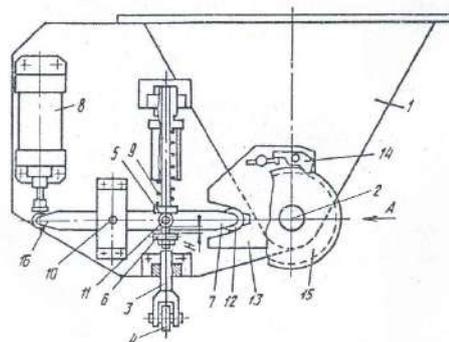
Устройство для подачи порошкообразных материалов в качающийся кристаллизатор [8]: 1- бункер; 2- шнековый питатель; 3- штанга-толкатель; 4- ролик; 5 и 6- упоры; 7- двулучий рычаг; 8- пневмоцилиндр; 9- пружина; 10- ось; 11 и 12- ролики; 13- коромысло; 14- собачка; 15- храповое колесо; 16- ролик
